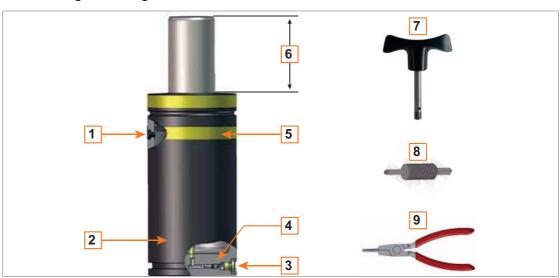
Bestandteile Gasdruckfeder DS / Benötigte Werkzeuge
